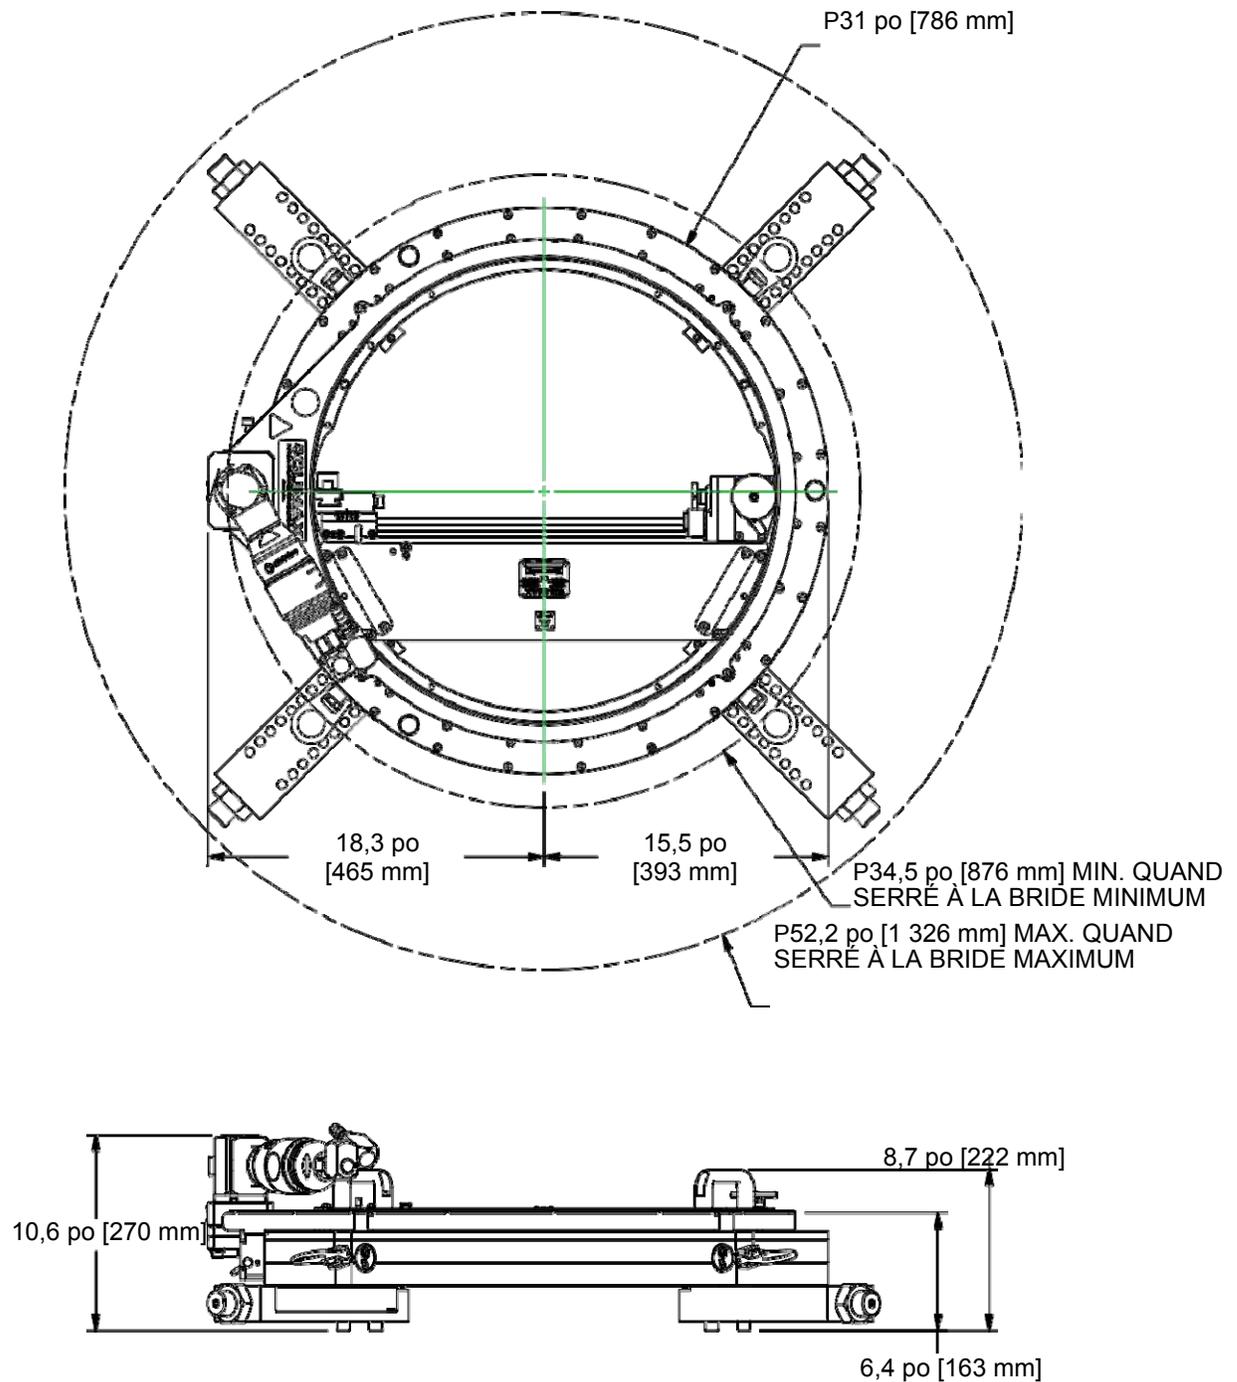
DIMENSIONS DE LA MACHINE FF3600 AVEC MOTEUR PNEUMATIQUE À ANGLE DROIT
